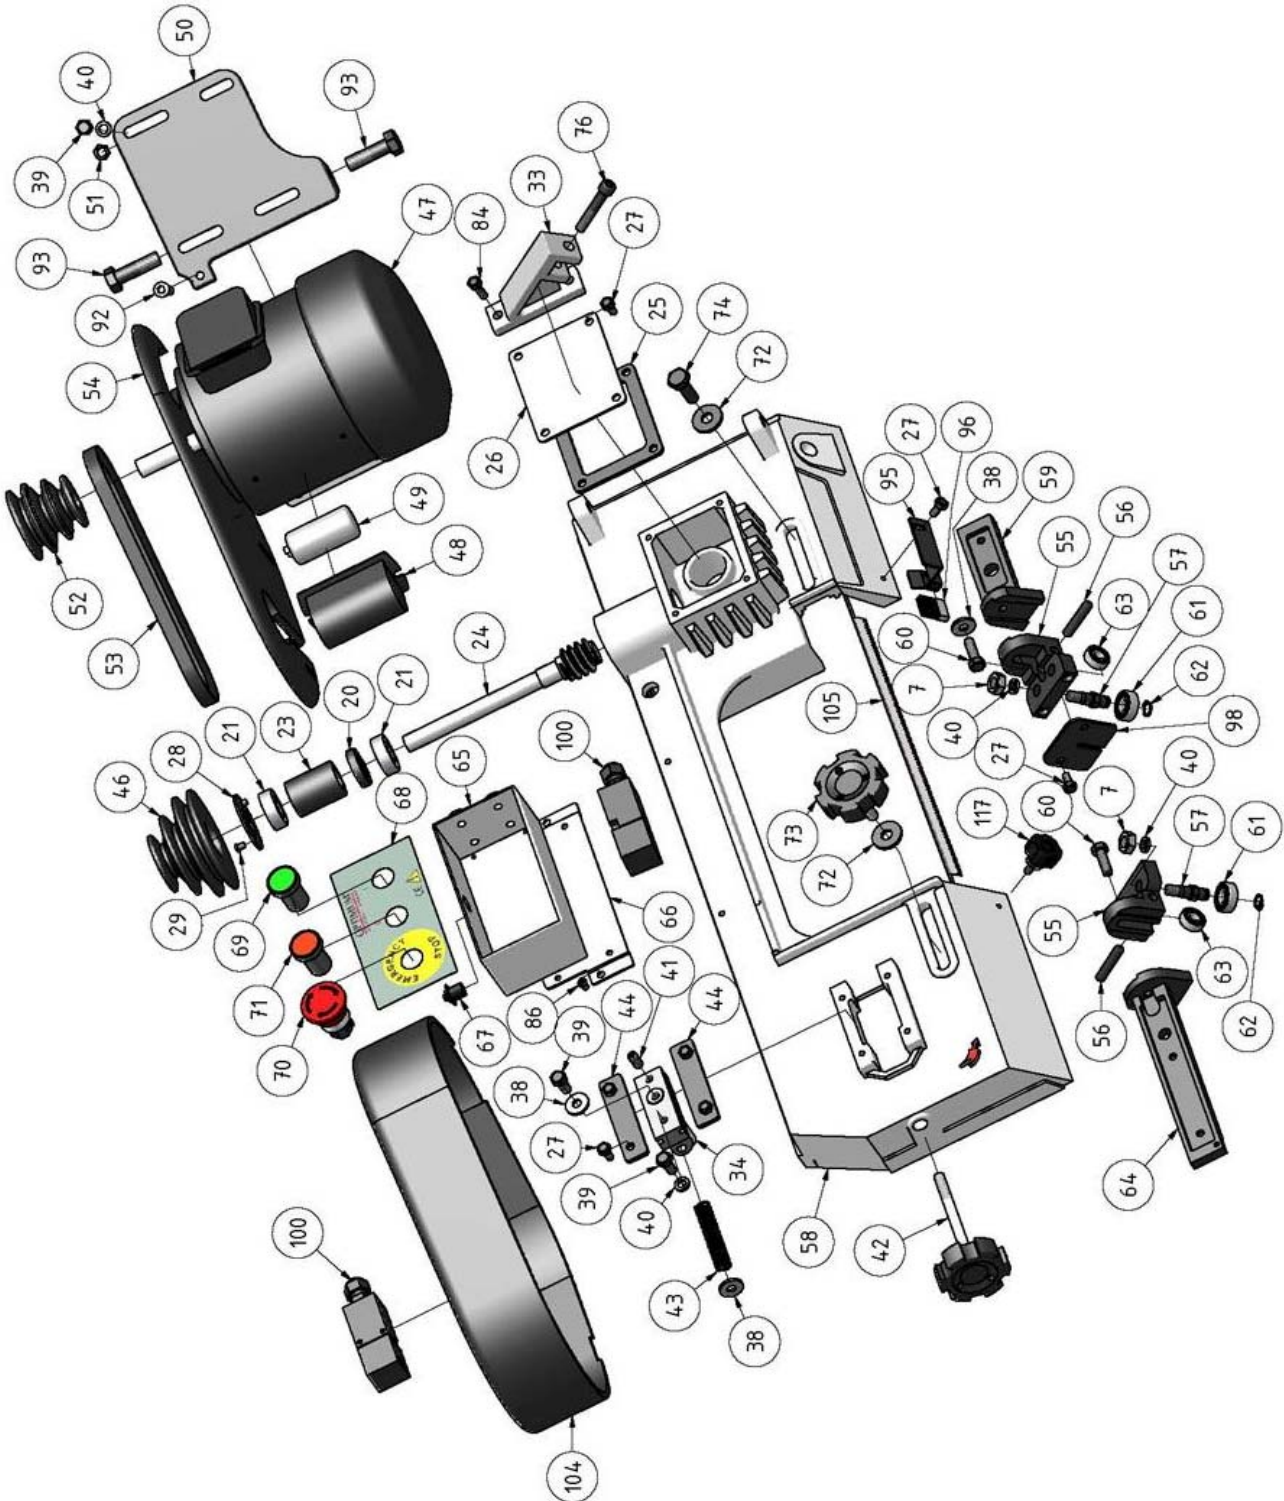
Ersatzteilzeichnung 1 von 4 - Parts drawing 1 of 4
